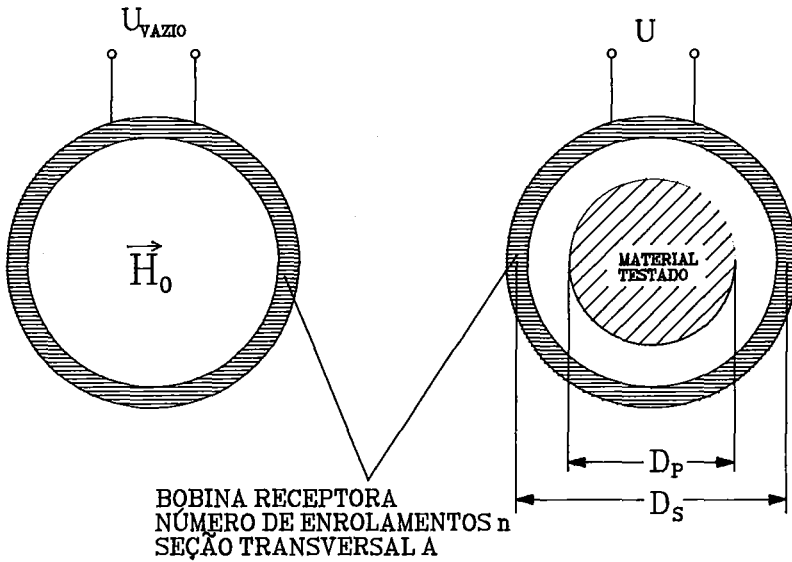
DISPOSITIVO DE ENSAIO COM SONDA EXTERNA
